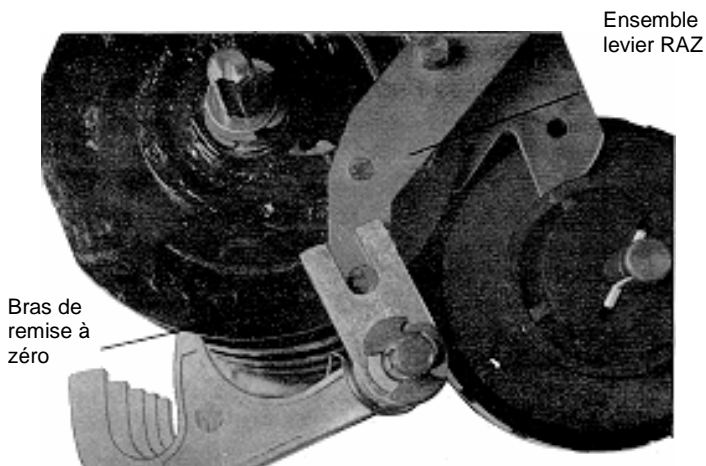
Engrenement goupille ensemble levier de remise à zéro
